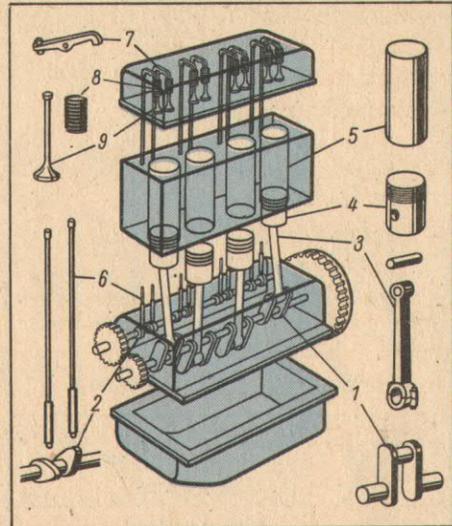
/1 Explosivdarstellung des Verbrennungsmotors (1) Kurbelwelle; (2) Nockenwelle; (3) Pleuelstange; (4) Kolben; (5) Zylinderlaufbuchse; (6) Stößelstange; (7) Kipphebel; (8) Ventilsfeder; (9) Ventil
